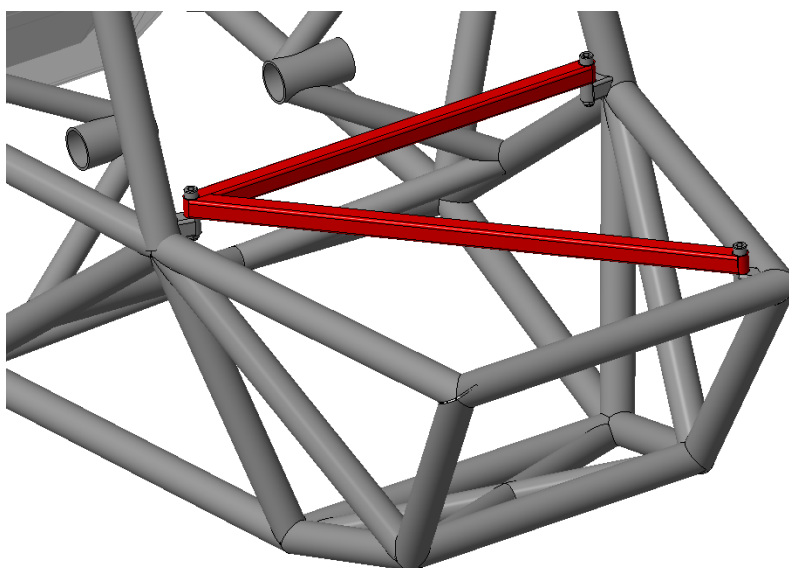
Konstrukční řešení zadního horního bodu zadního zavěšení
